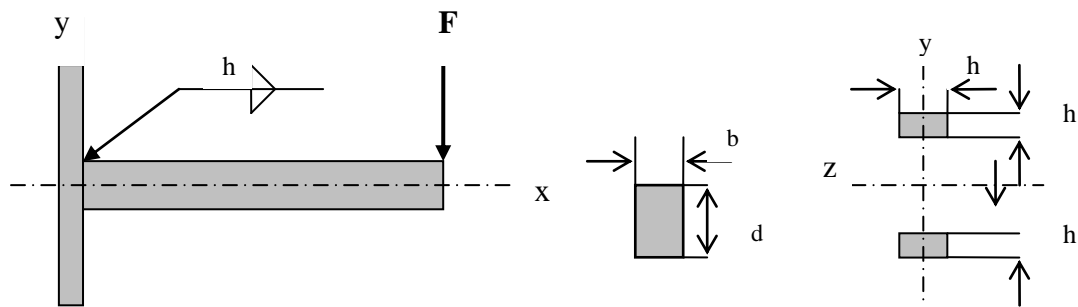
Diagrama de soldadura – eje/hélice
